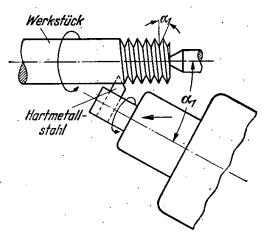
Gewindewirbeln. Umlaufendes Hartmetallwerkzeug mit einem Zahn.
